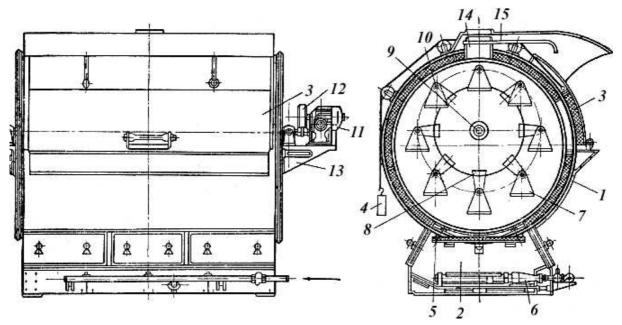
Ротаційна піч К7-ФП2-Г: 1 — циліндричний корпус; 2 — опора; 3 — піднімальні дверцята; 4 — противага; 5 — прохід із відбивачем; 6 — газові пальники; 7 — полиці ротора; 8 — диски ротора; 9 — вал; 10 — стрижні; 11 — електродвигун; 12 — редуктор; 13 — стійка; 14 — труба; 15 — засувка
